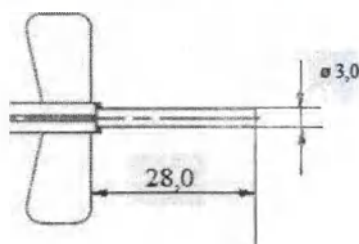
а - Чертеж колпачка с габаритными размерами, мм
